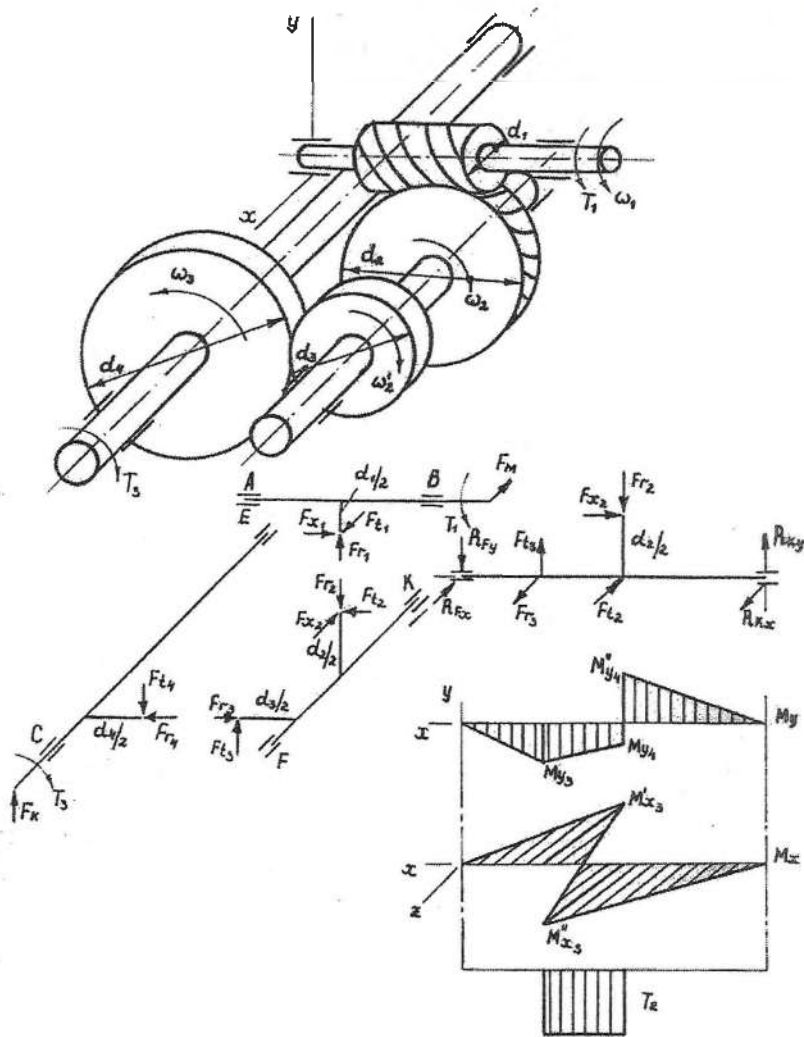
Червячно-зубчатая передача со второй цилиндрической прямозубой ступенью.
